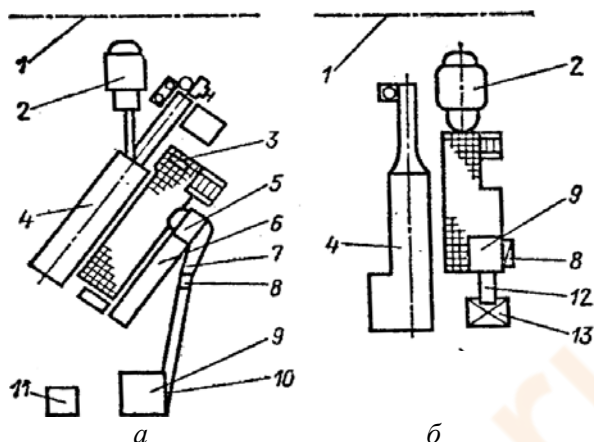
Расстановка комплекса оборудования для литья под давлением:
